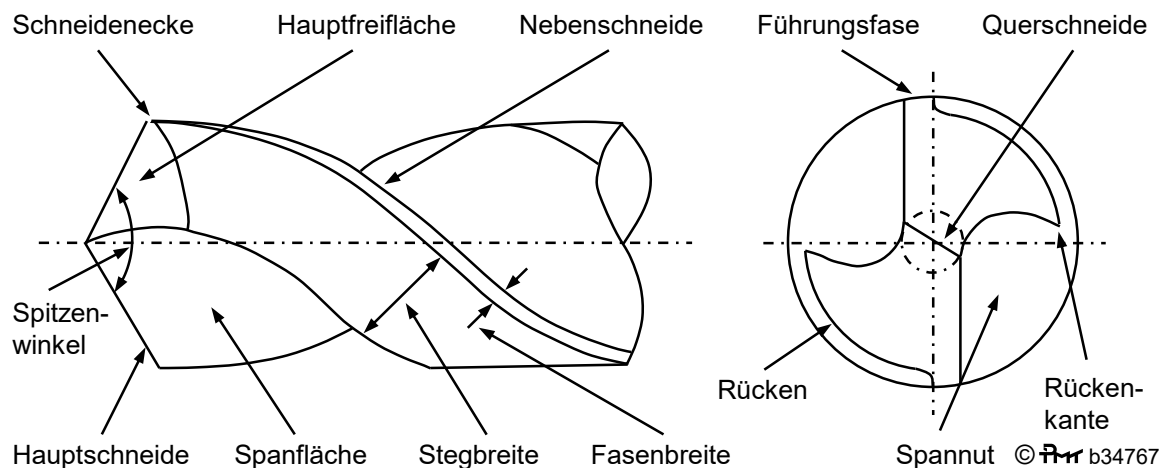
Bezeichnungen am Bohrwerkzeug [Wes06]
